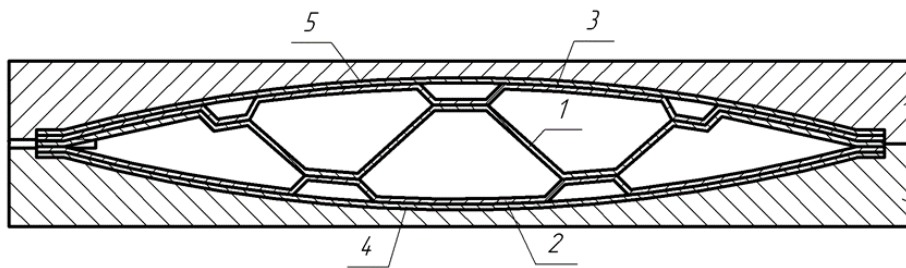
Пакет із п'яти листів на стадії формування: 1 – лист наповнювача, 2, 3 – внутрішня обшивка, 4,5 – зовнішня обшивка.
